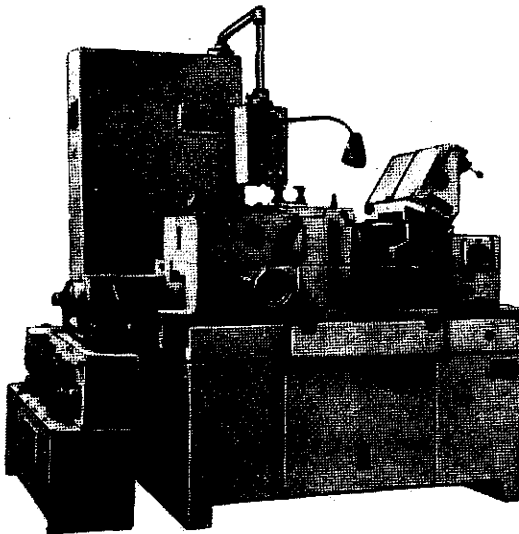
Круглошлифовальный бесцентровый станок ЗМ182
